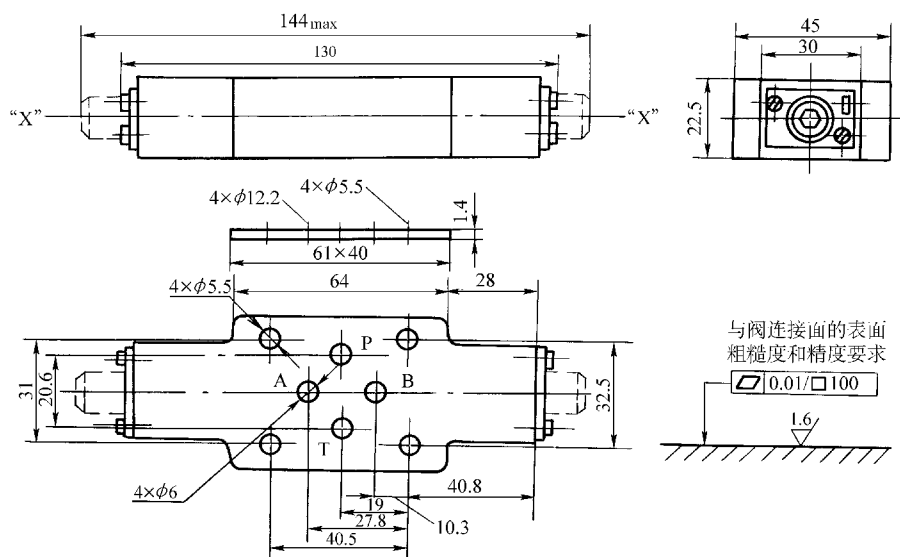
Z2FS6 型叠加式节流阀的外形尺寸
